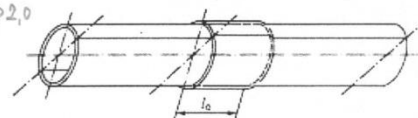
Probă — Îmbinare prin suprapunere simplă
